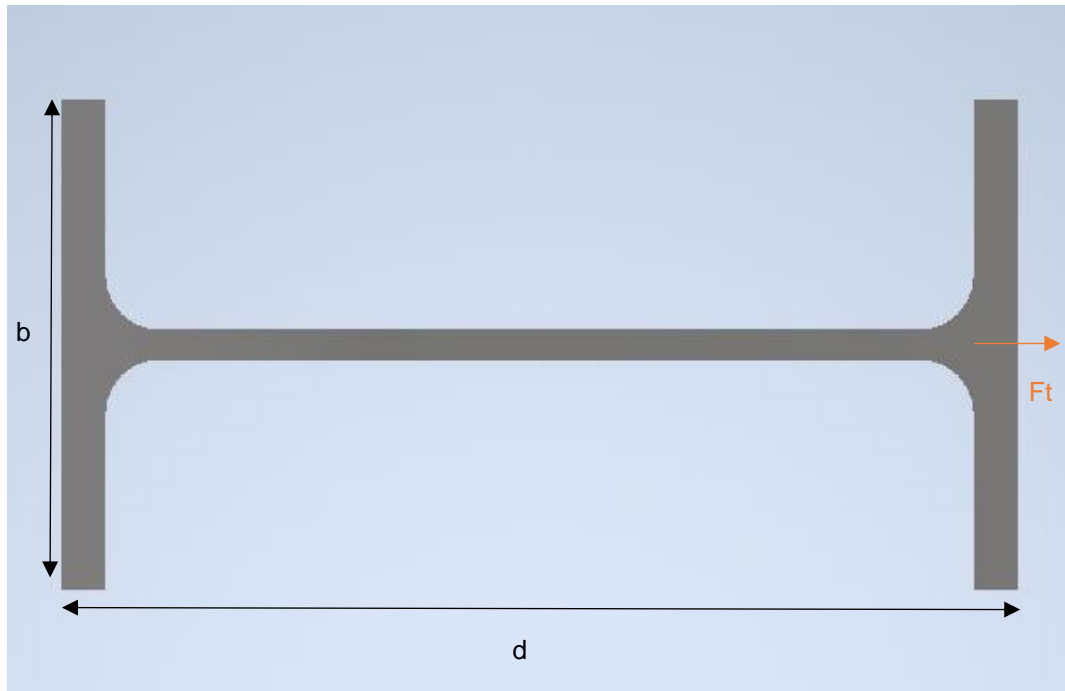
Diagrama de cuerpo libre para cálculo de soldadura de la viga IPE.
